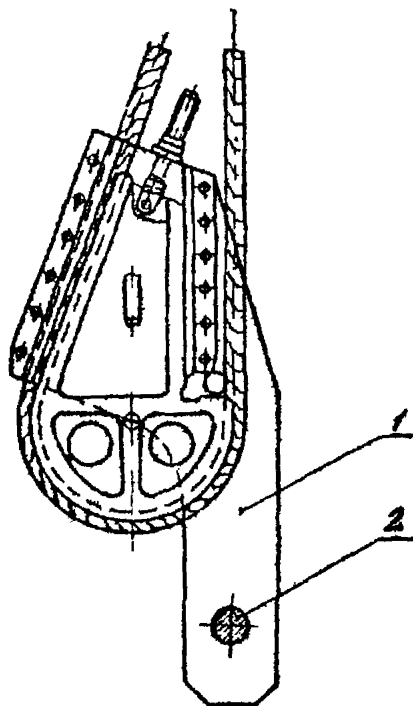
Коуш ККБ: 1 - лист (щека); 2 - валик.
